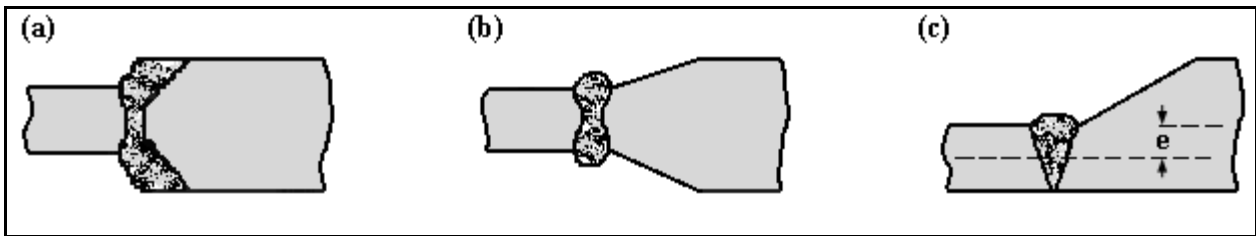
Soldaduras a tope entre placas de diferente espesor. (a) Soldadura hecha directamente entre placas de diferente espesor, (b) junta a tope alineada axialmente con el espesor de la placa rebajado, (c) junta desalineada con el espesor de la placa rebajado.
